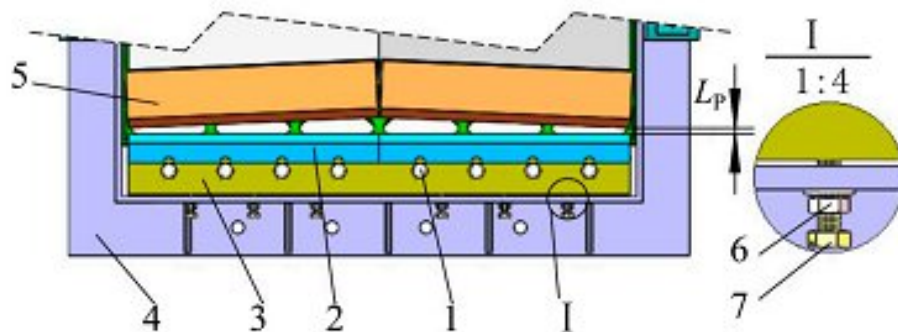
Схематична діаграма конструкції вузла регулювання зазору між рухомим і нерухомим ножами
